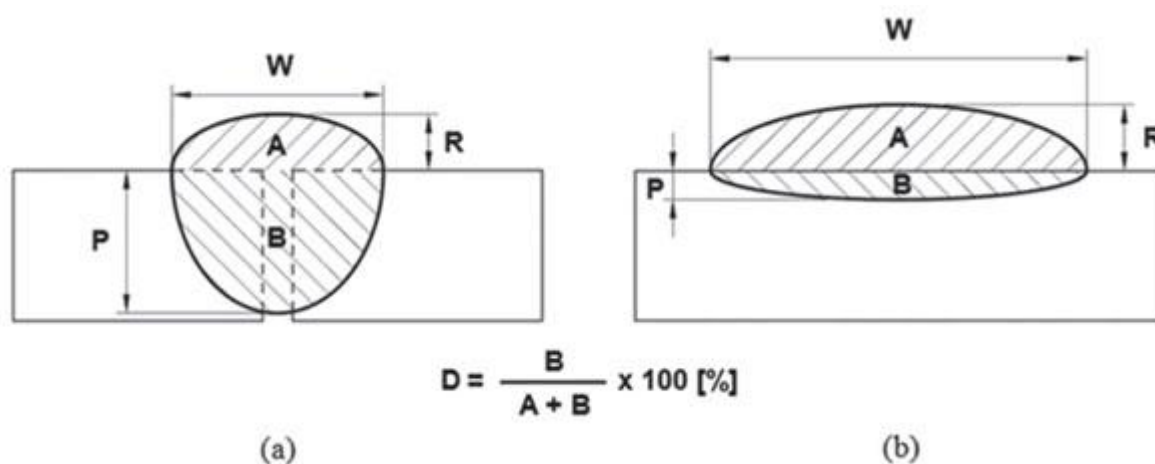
Perfil geométrico desejado do cordão de solda: a)união da junta soldada(aplicações convencionais); b) soldagem de revestimento (Gomes, 2010).
